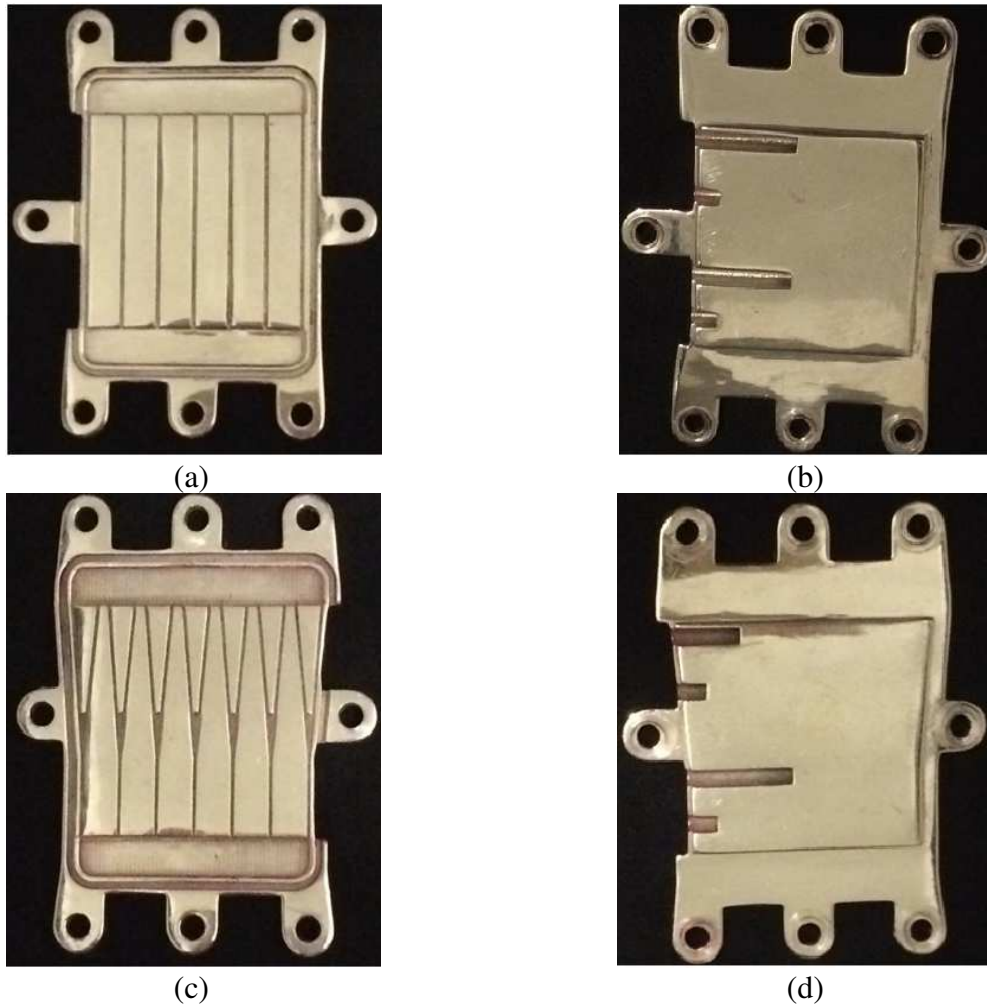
Trocador de calor de microcanais: (a) canais retos - vista superior; (b) canais retos - vista inferior; (c) canais em Y com um nível de ramificação - vista superior; (d) canais em Y com um nível de ramificação - vista inferior
